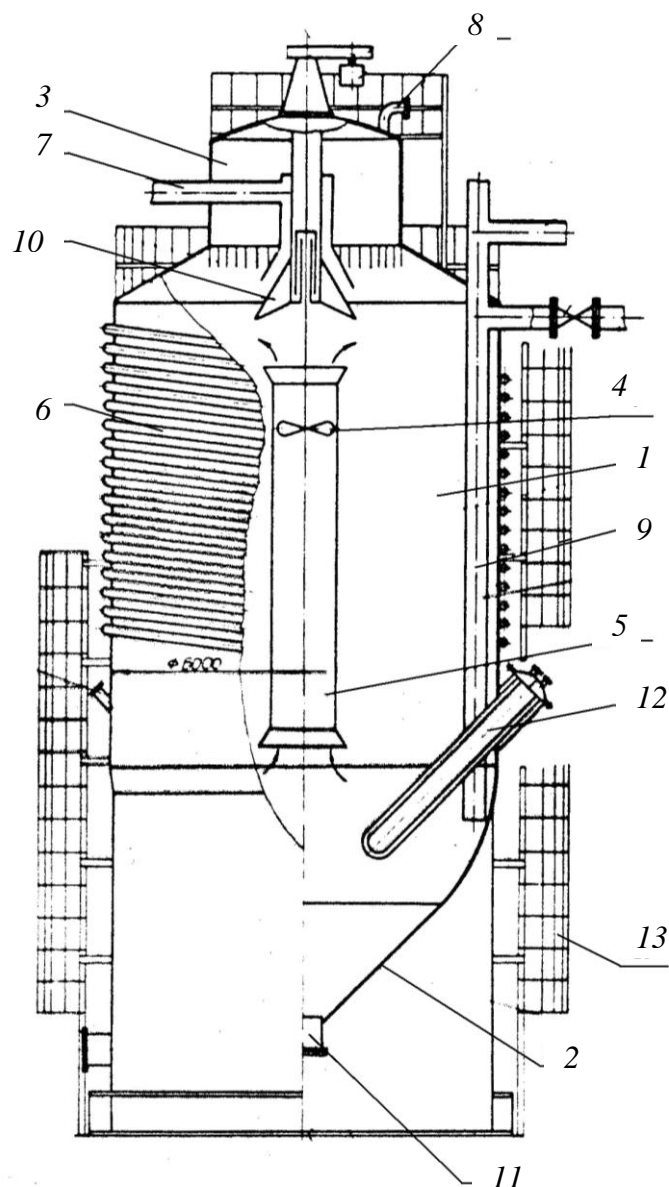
Конструкция метантенка: 1 – корпус; 2 – коническое днище; 3 – горловина; 4 – пропеллерная мешалка; 5 – циркуляционная труба; 6 – змеевиковый теплообменник; 7 – загрузочный патрубок; 8 – патрубок для отвода биогаза; 9 – труба выгрузки сброженной массы; 10 – устройство для коркоразрушения; 11 – сливной патрубок; 12 – погружной теплообменник; 13 – теплоизоляция
